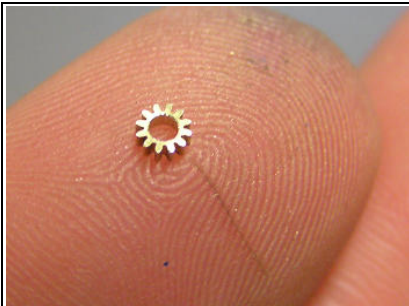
Zahnrad Z12 mit 1,5mm Innendurchmesser soll streng auf die Motorwelle passen. (Presspassung ohne Kleber, damit die Abtriebswelle nicht mit dem Getriebegehäuse verklebt)
